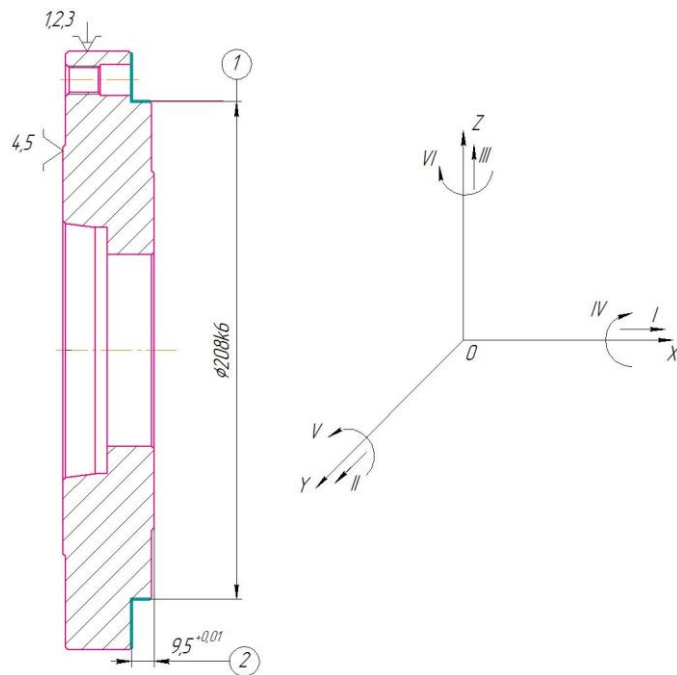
Схема базування заготовки в мембранному патроні
